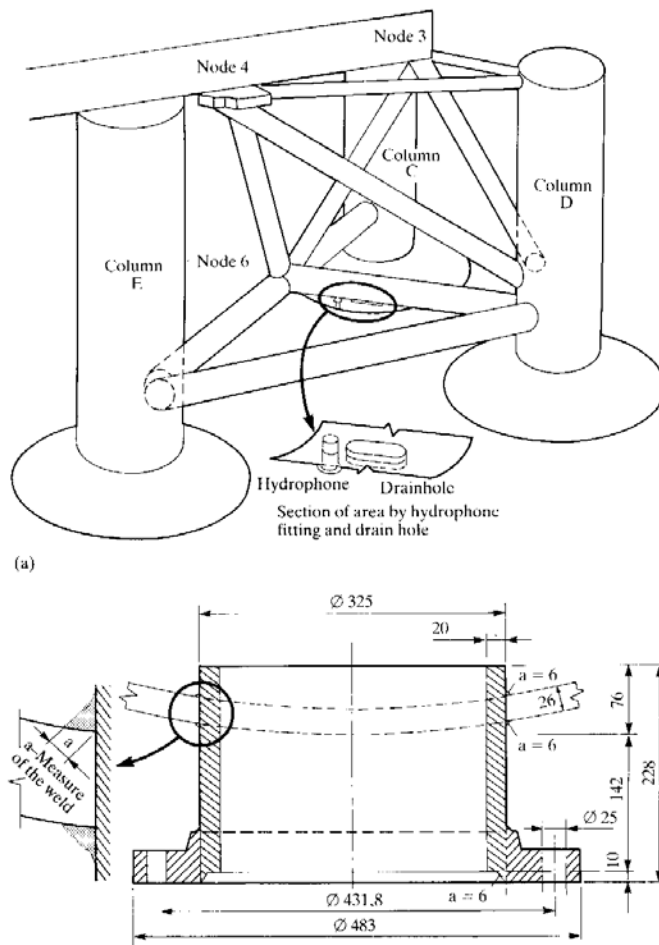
Ubicación de la brida en el miembro estructural principal y dimensiones
